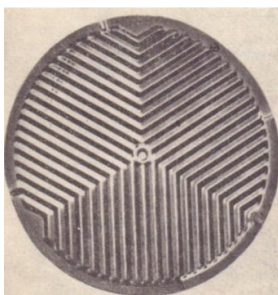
Пластина сварного ПТА для колонны синтеза аммиака
